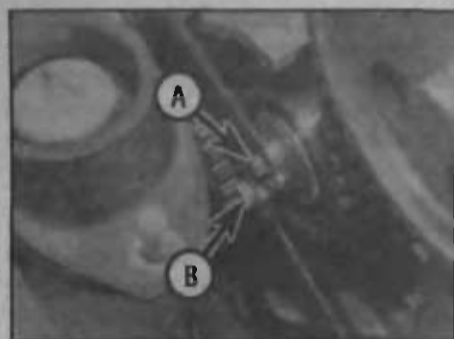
Использование гаечных ключей для ослабления гайки (В) крепления шкива механизма натяжения и для поворота стержня квадратного сечения на 8 мм (В) против часовой стрелки при регулировке натяжения зубчатого ремня
